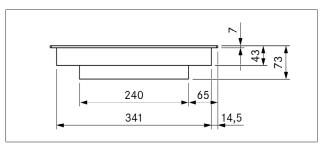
Dimensões do aparelho PKC3, vista dianteira
